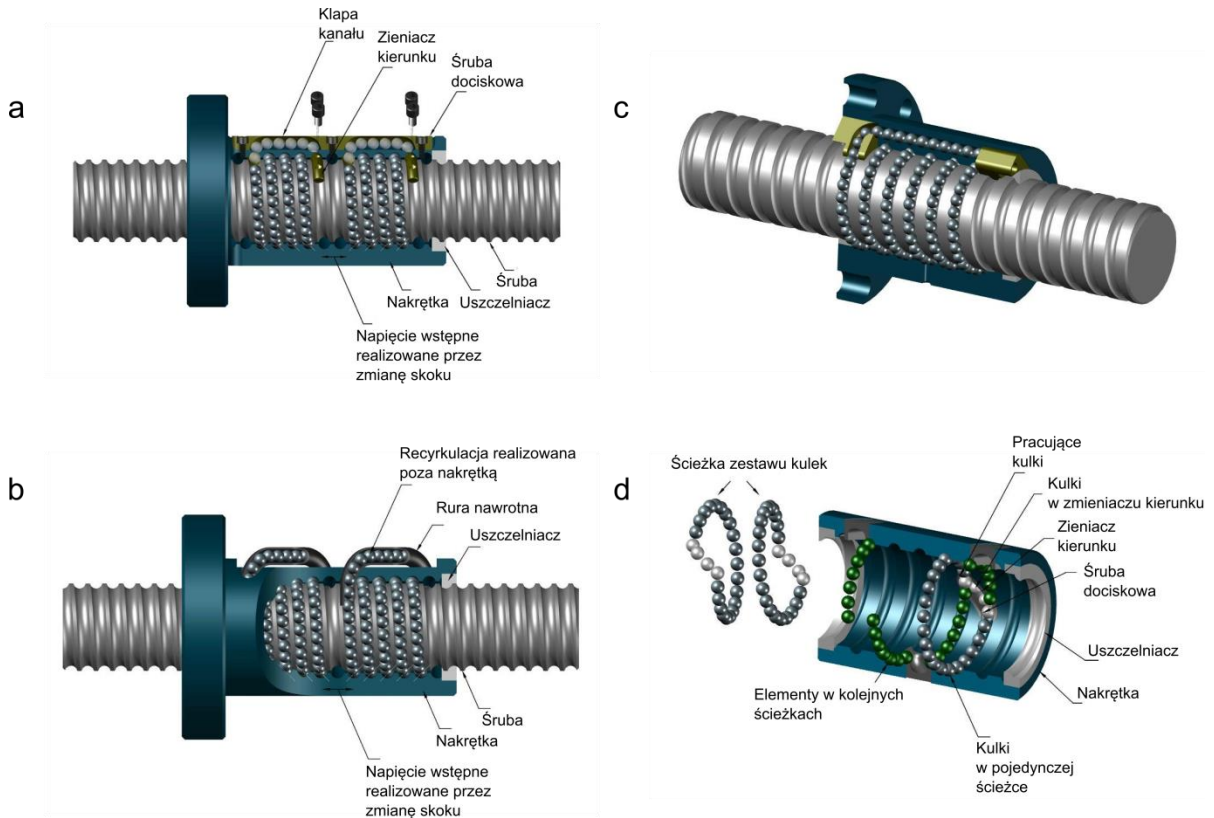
Podstawowe składniki mechanizmu śrubowo-tocznego
